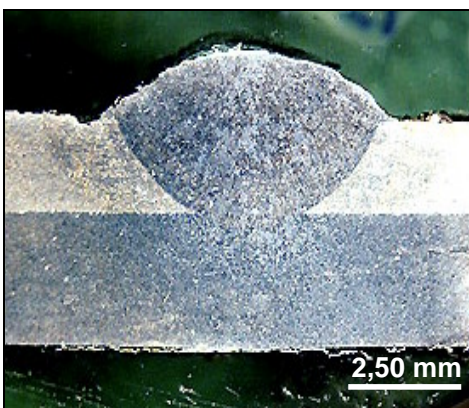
União metalúrgica entre solda, revestimento e substrato. Parâmetros de soldagem: 80 A; 26,1 volts; 17 cm/min.
